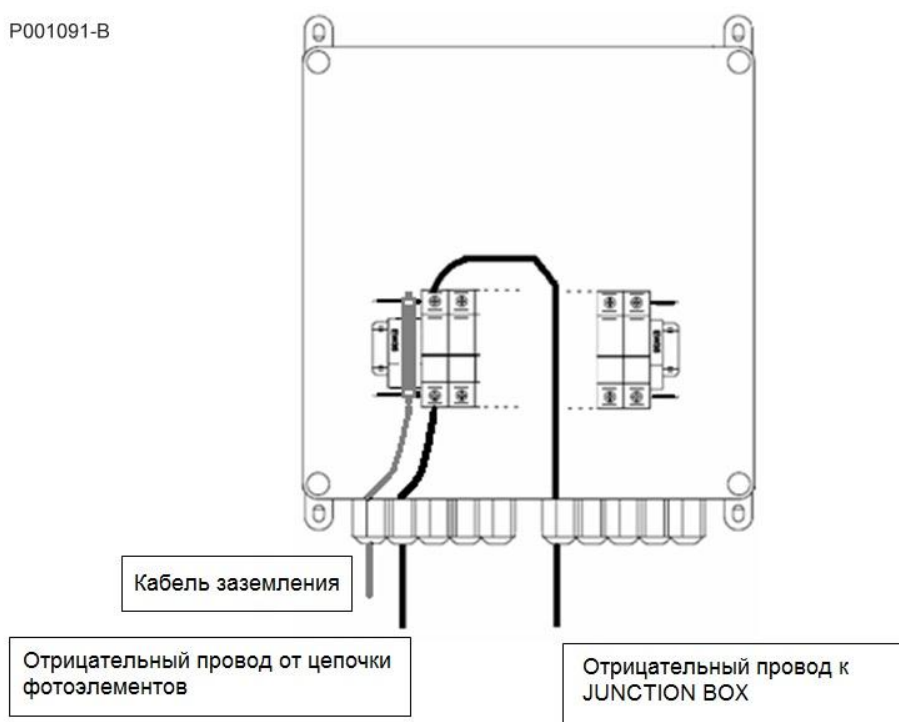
Схема подключения отрицательного полюса цепочки фотоэлементов через FUSE BOX к коммуникатору.
